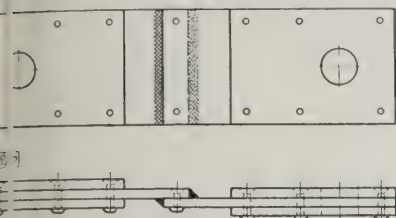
Überlappung mit 19 mm-Nieten, leichte senkrechte Schweißung.
